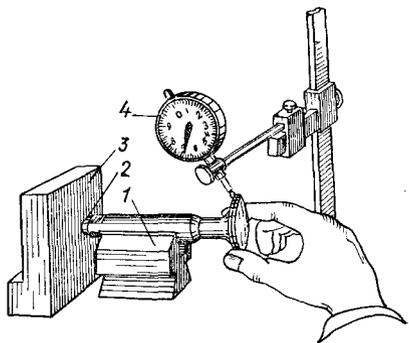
Проверка бие-ния рабочей фаски клапана:
